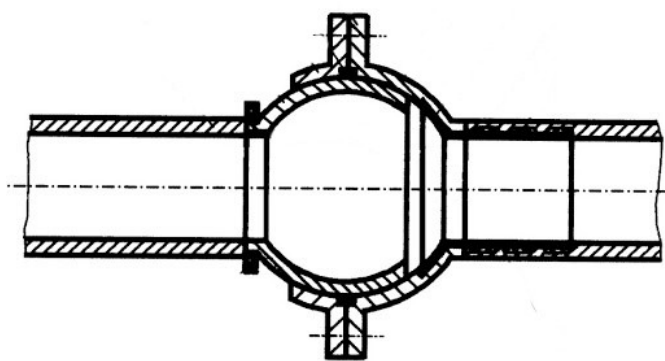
Чертеж шарнирного подвижного соединения труб
